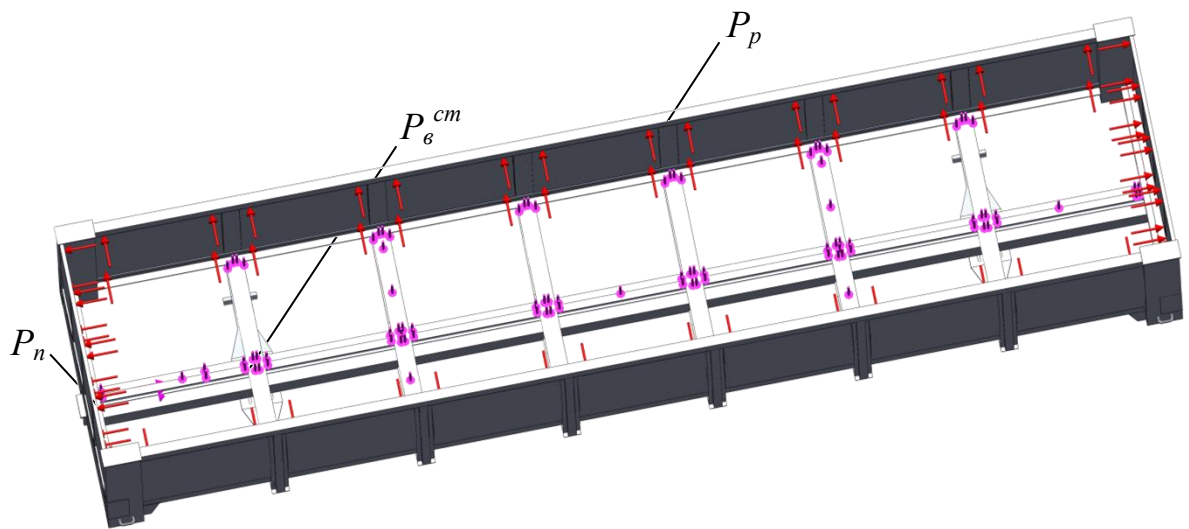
Розрахункова схема несучої конструкції напіввагона
